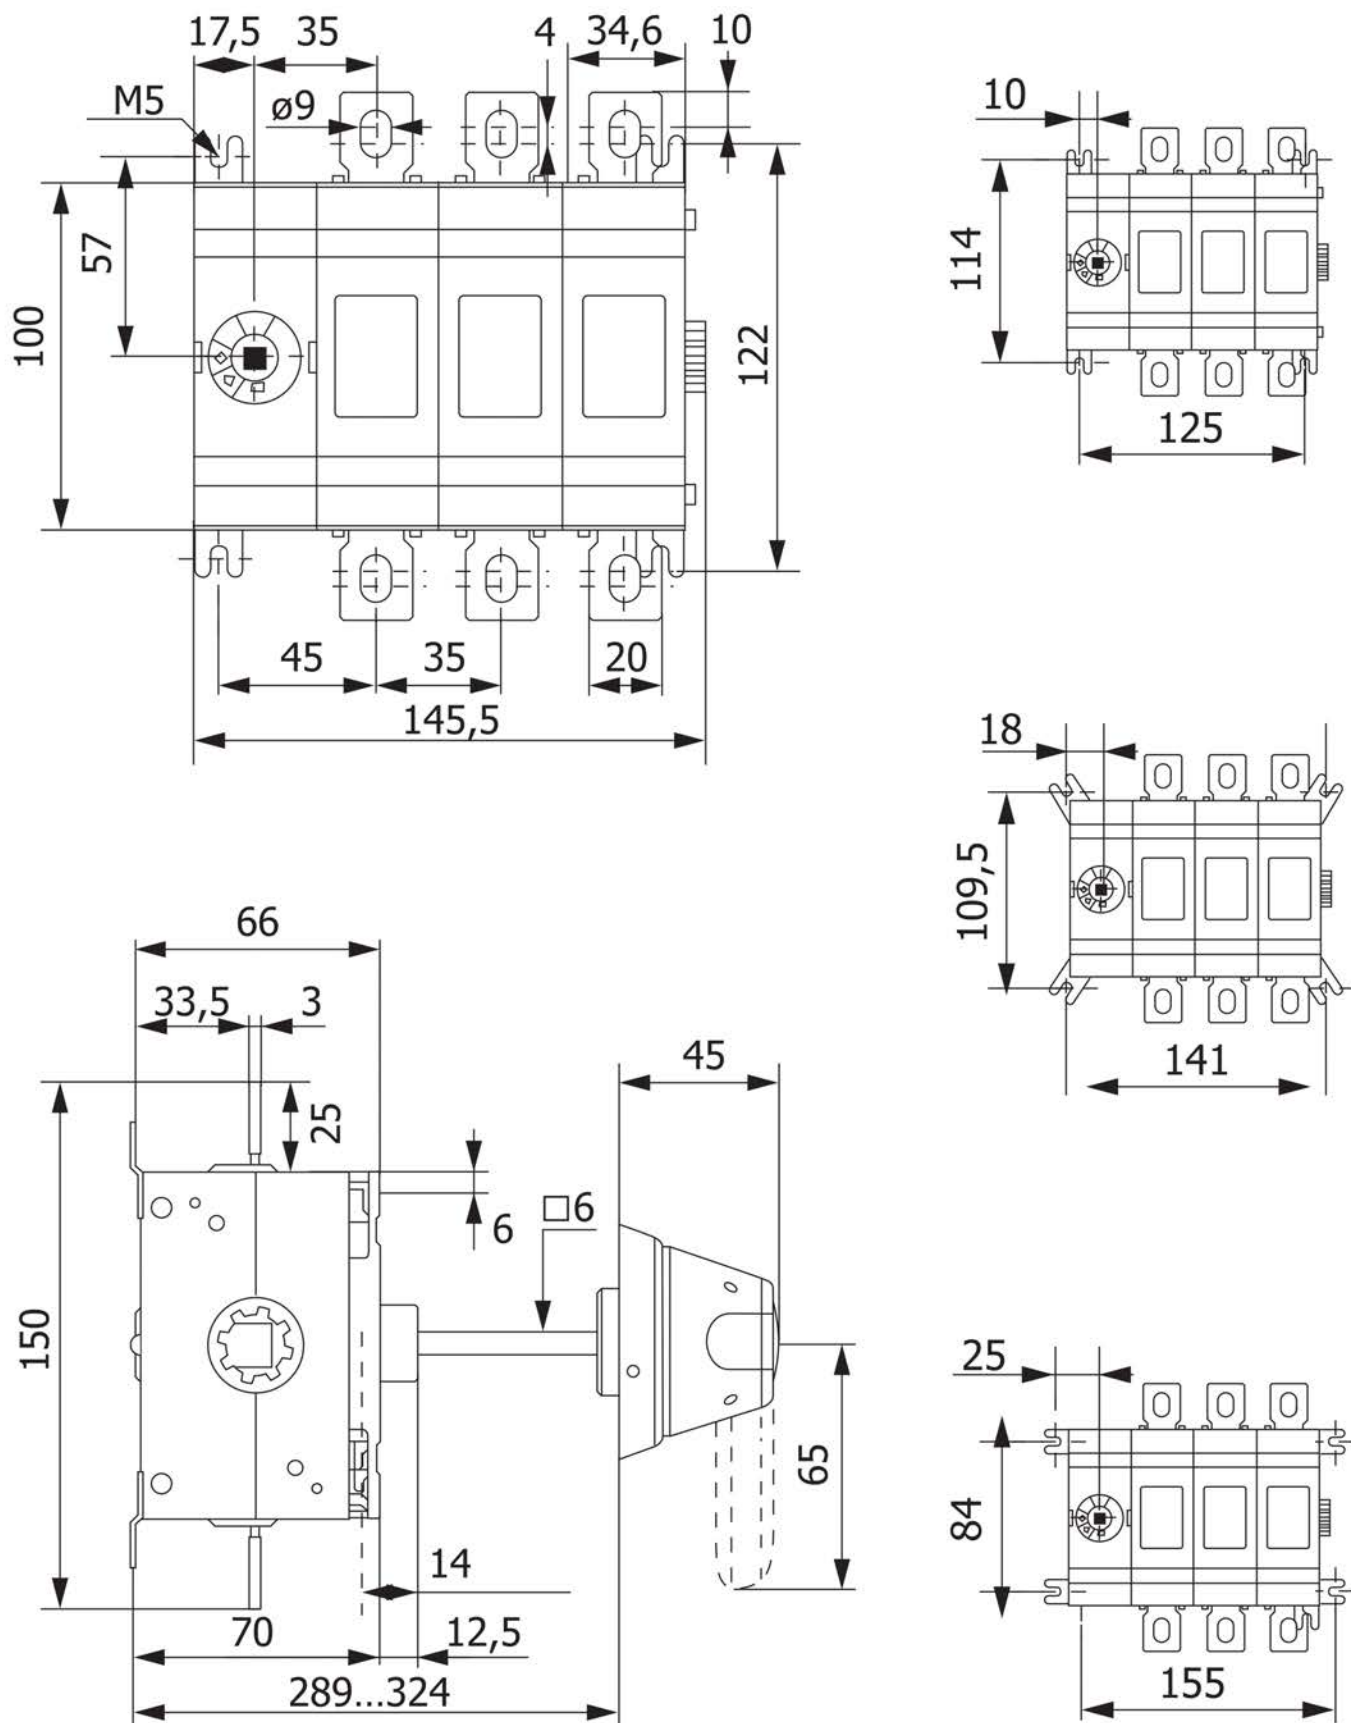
Габаритные и установочные размеры рубильников 160-250 А
